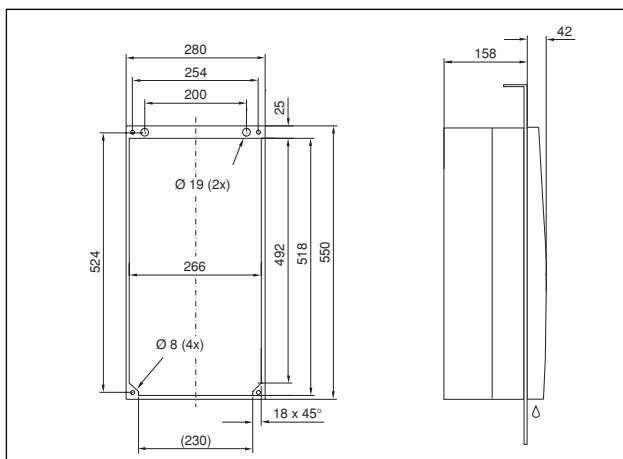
SK 3303.xxx, SK 3361.xxx til fuld indbygning
